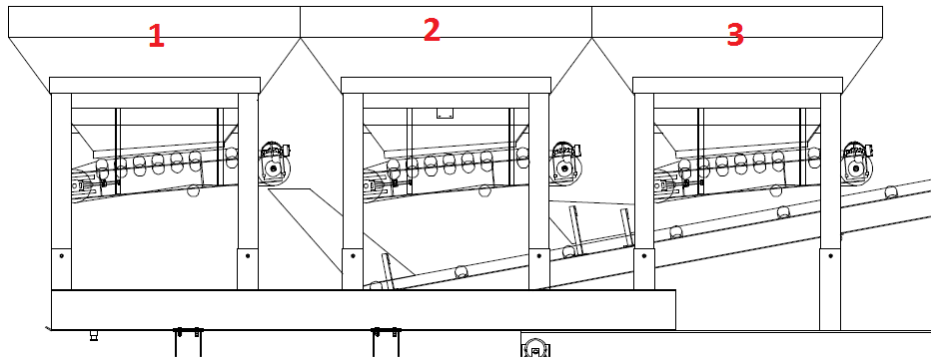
7. Distribución de tolvas en planta de suelos
